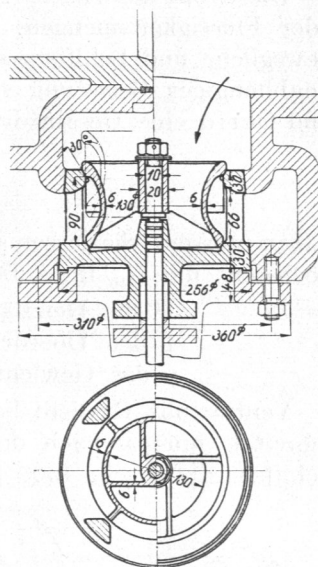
Doppelsitzauslaßventil am Niederdruckzylinder der Maschine Tafel I. M. 1:10.
